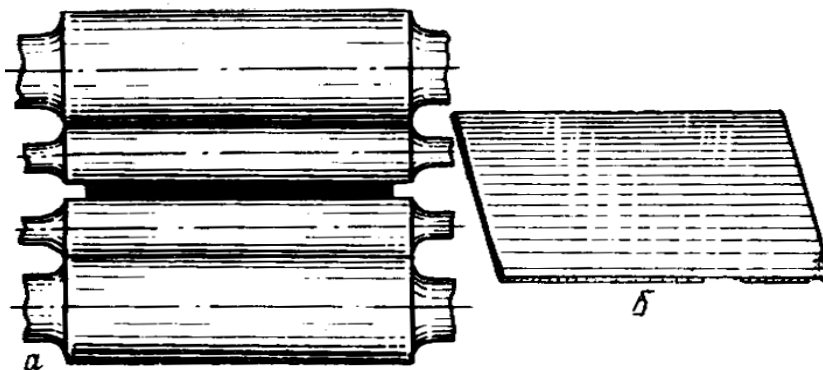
Вплив опуклої бочки валка на якість викочування й поверхня штаби
